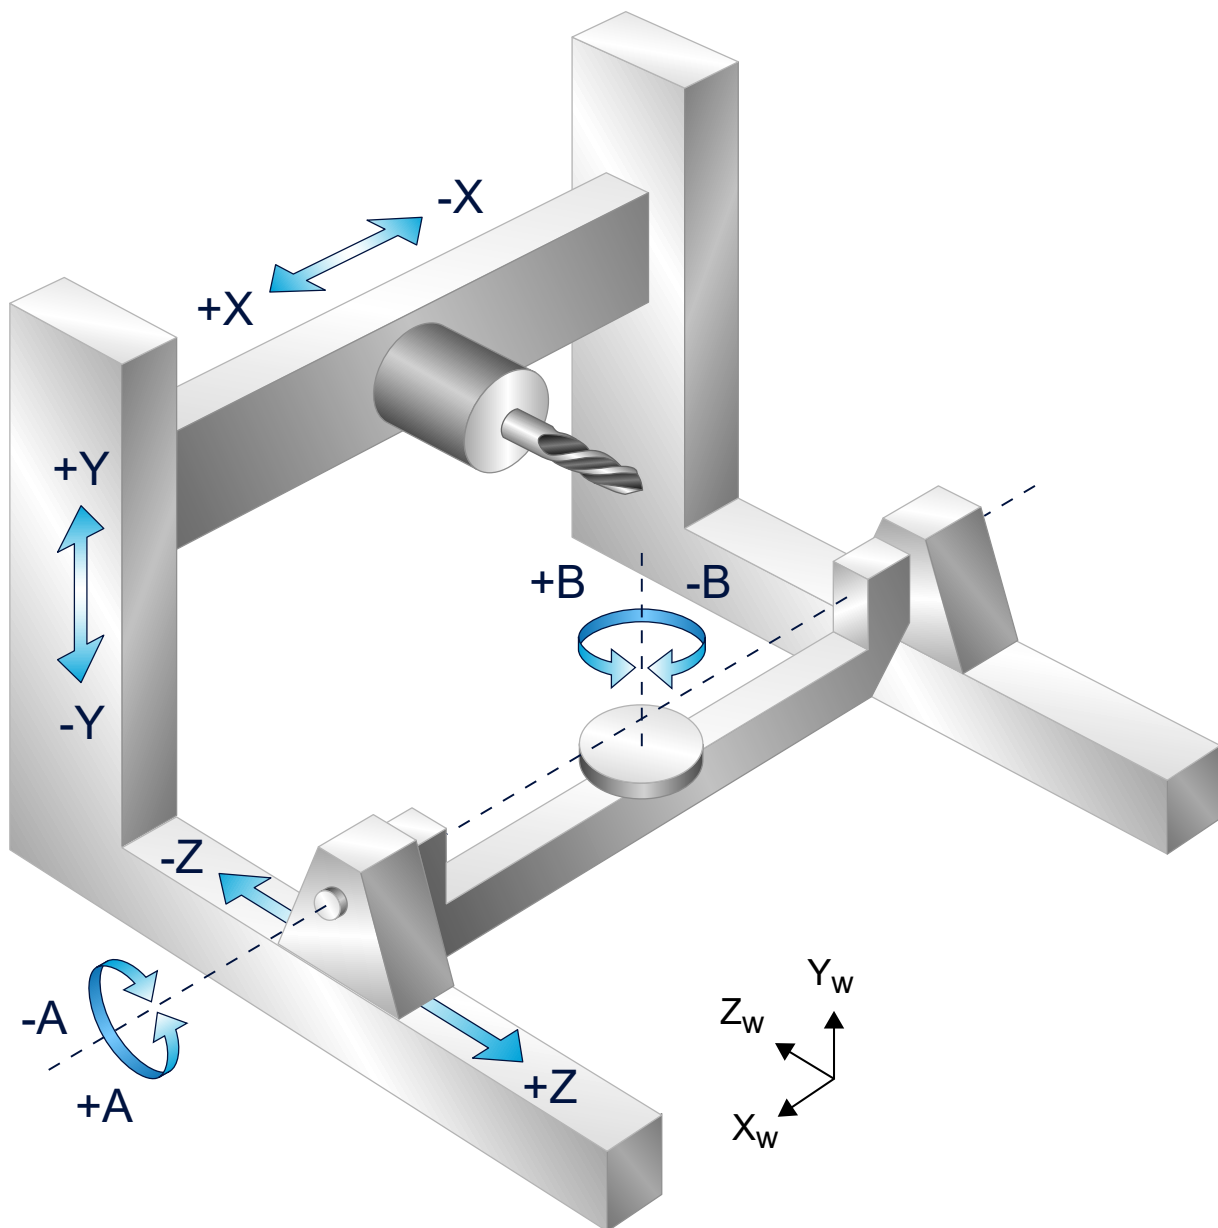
Kinematik der 5-achsigen Fräsmaschine
